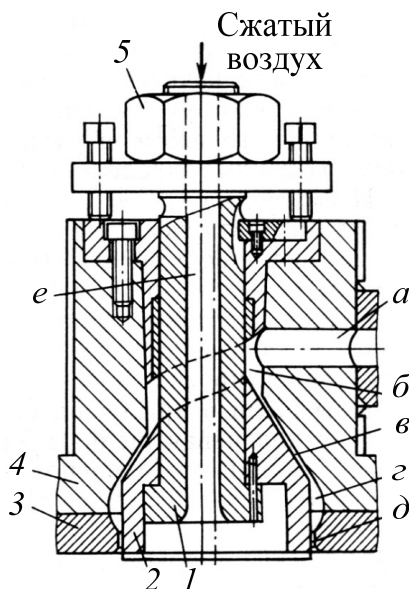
Головка для получения трубчатой заготовки со скошенным конусом и составным дорном:
